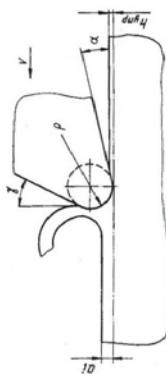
Схема врізання зуба фрезами при зубофрезеруванні зубчастих колес
